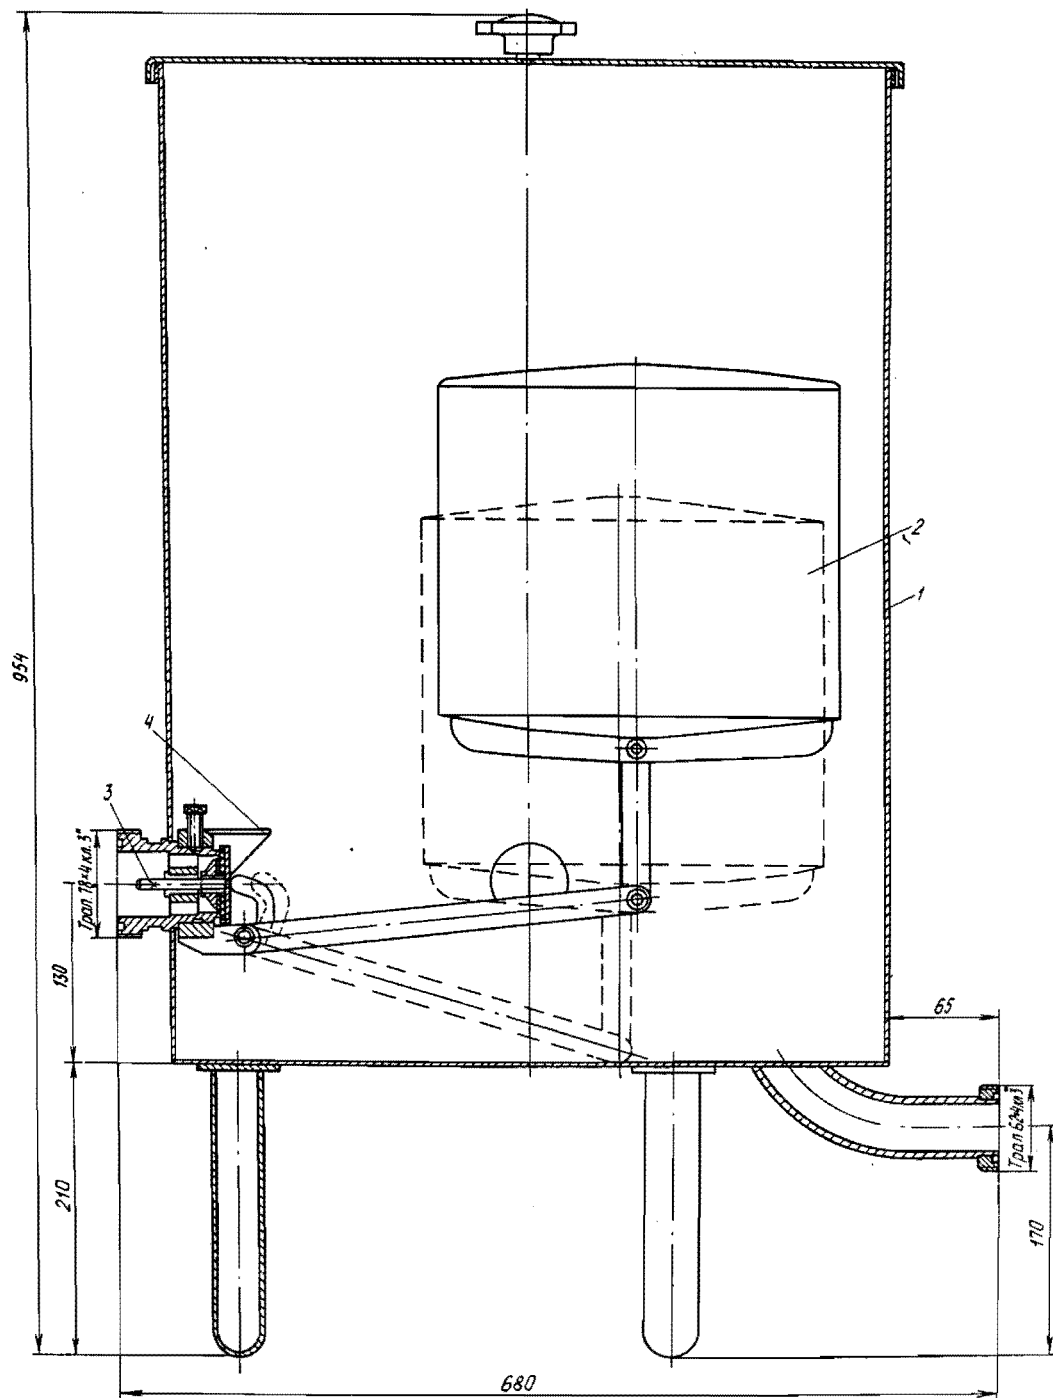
Общий вид уравнительного бака установки марки А1-ОКЛ-10:
